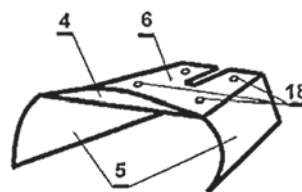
формователя-уплотнителя (в изометрии): 4 – козырек; 5 – корпус; 6 – крыша; 18 – отверстия
